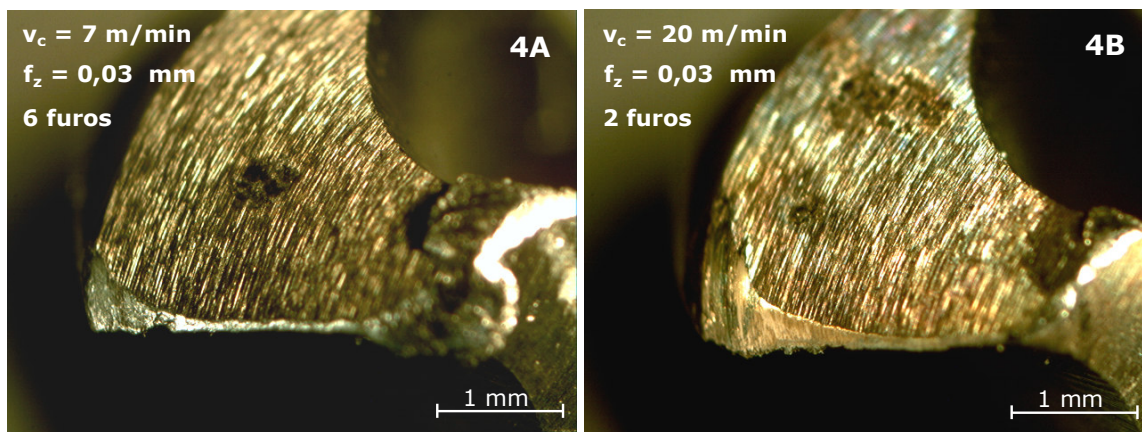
Desgaste de flanco da ferramenta na usinagem com diferentes parâmetros de corte.
